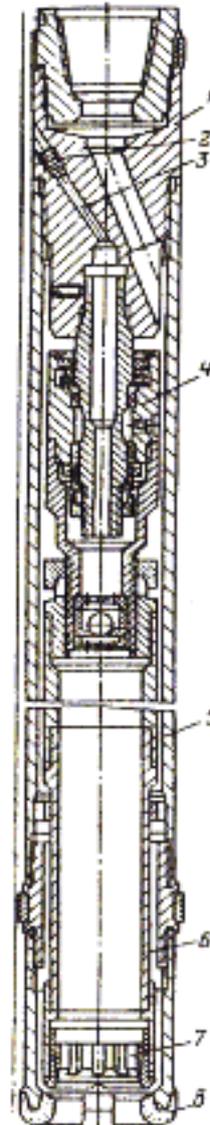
Двойная колонковая труба для алмазного бурения ТНД-2/0: 1 – переходник; 2 – пробка; 3 – боковой канал; 4 – подшипниковый узел; 5 – межтрубный зазор; 6 – керноприемная труба; 7 – кернорватель; 8 – коронка
